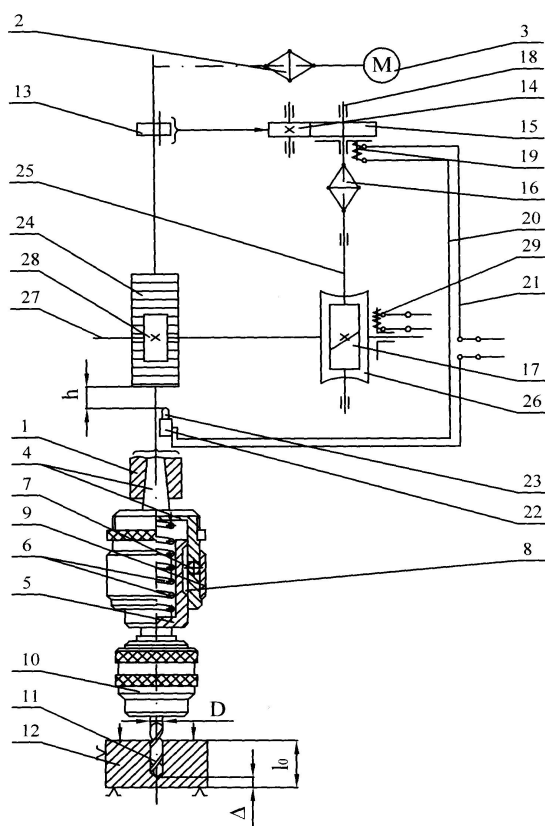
Механізм подачі шпинделя свердлильного верстата
